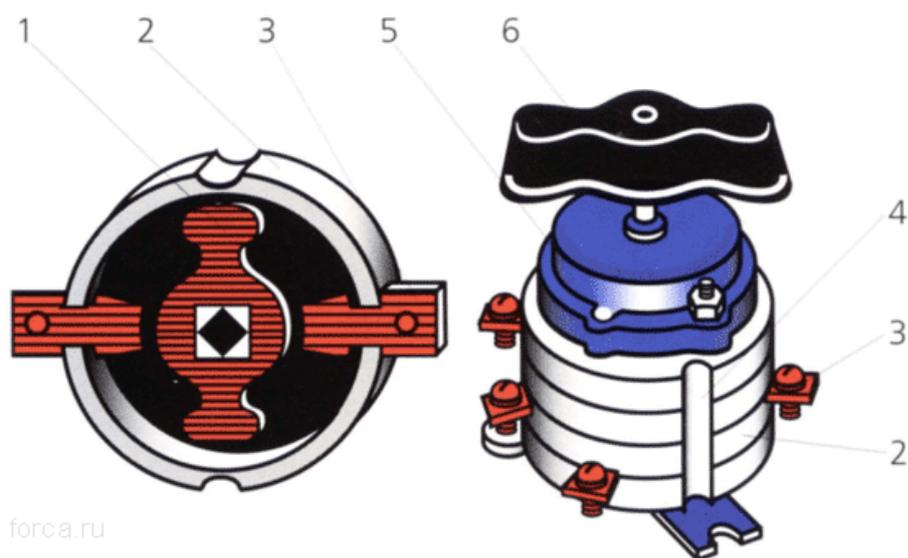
Устройство пакетного выключателя: 1 - подвижный контакт - нож; 2 - кольцо-пакет; 3 - неподвижный контакт; 4 - набор колец-пакетов; 5 - крышка с пружинной шайбой; 6 - рукоятка
